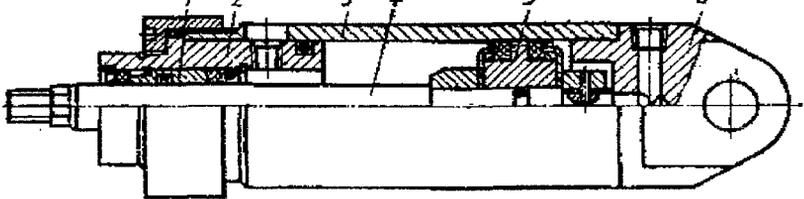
Конструкция гидроцилиндра типа ГЦ по ТУ2 – 053-1625-82Е [17]: гильза 3; шток 4; поршень 5; крышки 2 и 6; направляющие втулки 1.
